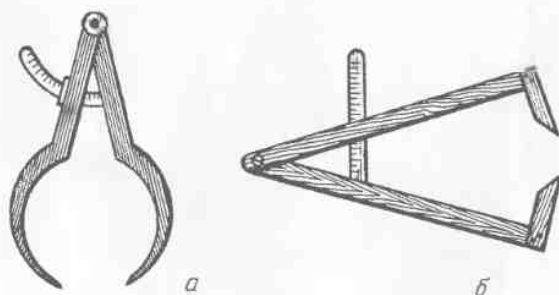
Кронциркуль: а — измерительный стандартный; б — самодельный для измерения толщины кривых стенок
